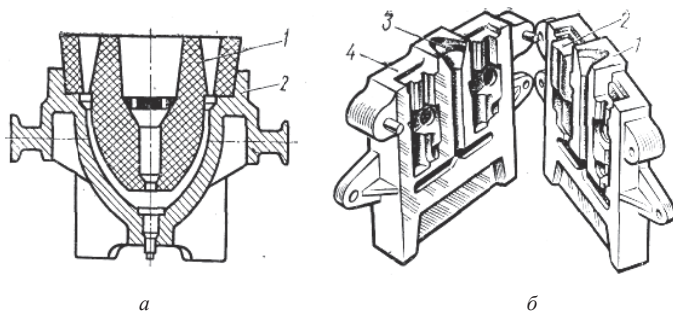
Кокили (металлические формы): а – неразъемный кокиль с отливками, вытряхиваемыми после остывания (1 – стержень; 2 – кокиль); б – разъемный кокиль (1 и 4 – полуформы; 2 – вставка; 3 – литниковая система)
